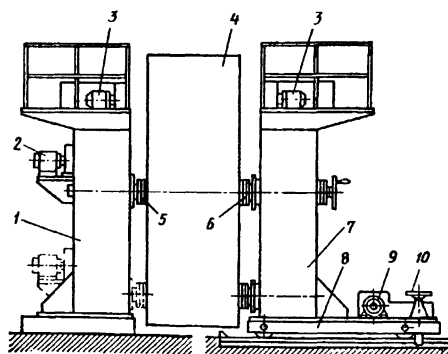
Двухстоечный кантователь с подъемными центрами:
